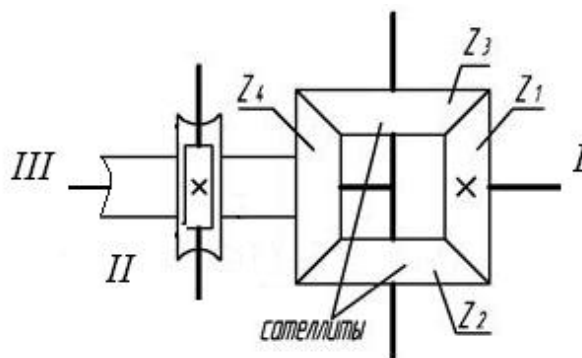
Дифференциальный механизм с коническими зубчатыми колесами.
